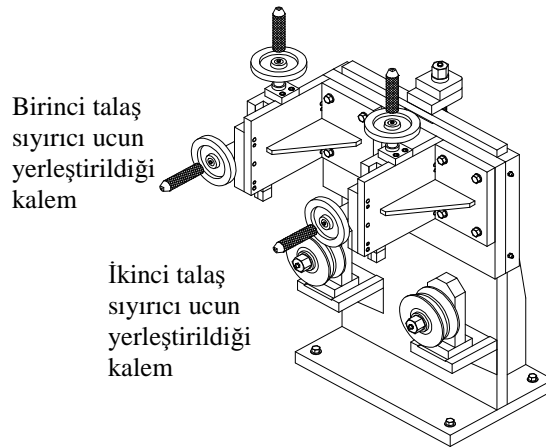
Kaynak grubu şekillendirme makara grubu [6]
